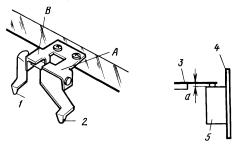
Элементы регулировки положения рычага определения типа используемой ленты:
